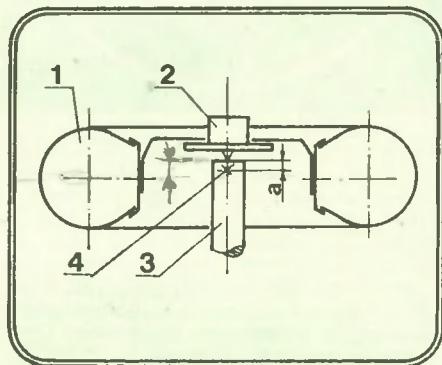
Схема балансировки колеса: 1 — колесо; 2 — приспособление; 3 — опора; 4 — центр тяжести колеса.
